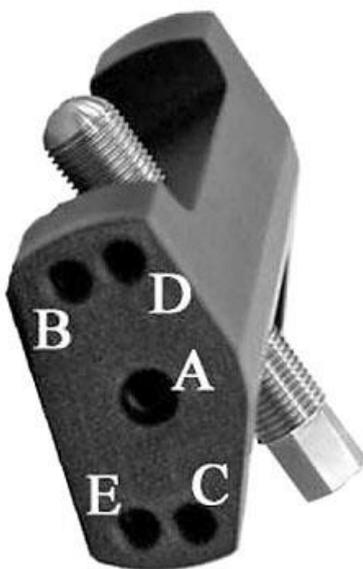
"Widerlagerstange" mit Gewindebohrungen für die Polhöhenanpassung
